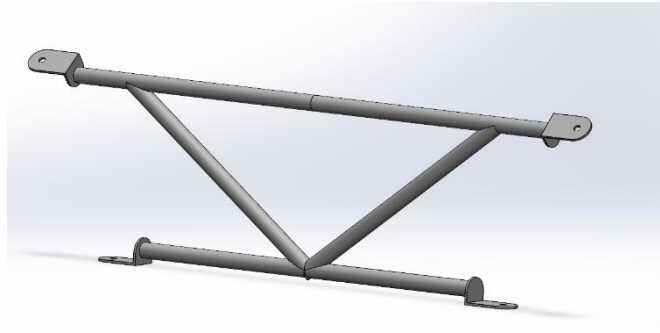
Ensamblaje final de la pieza en SolidWorks (1). [Fuente propia]
